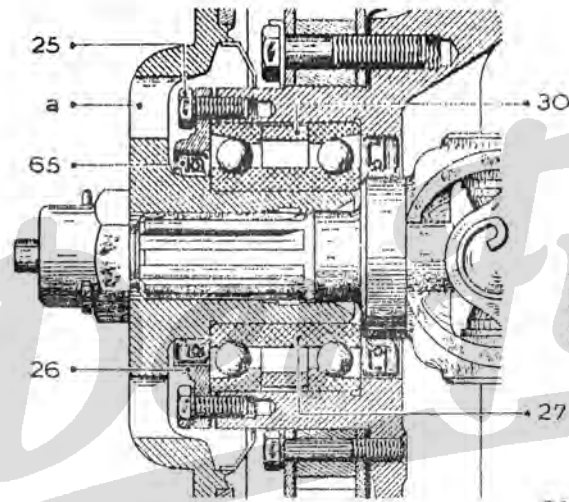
Doppel-Rollenlager mit Schrägrollen
